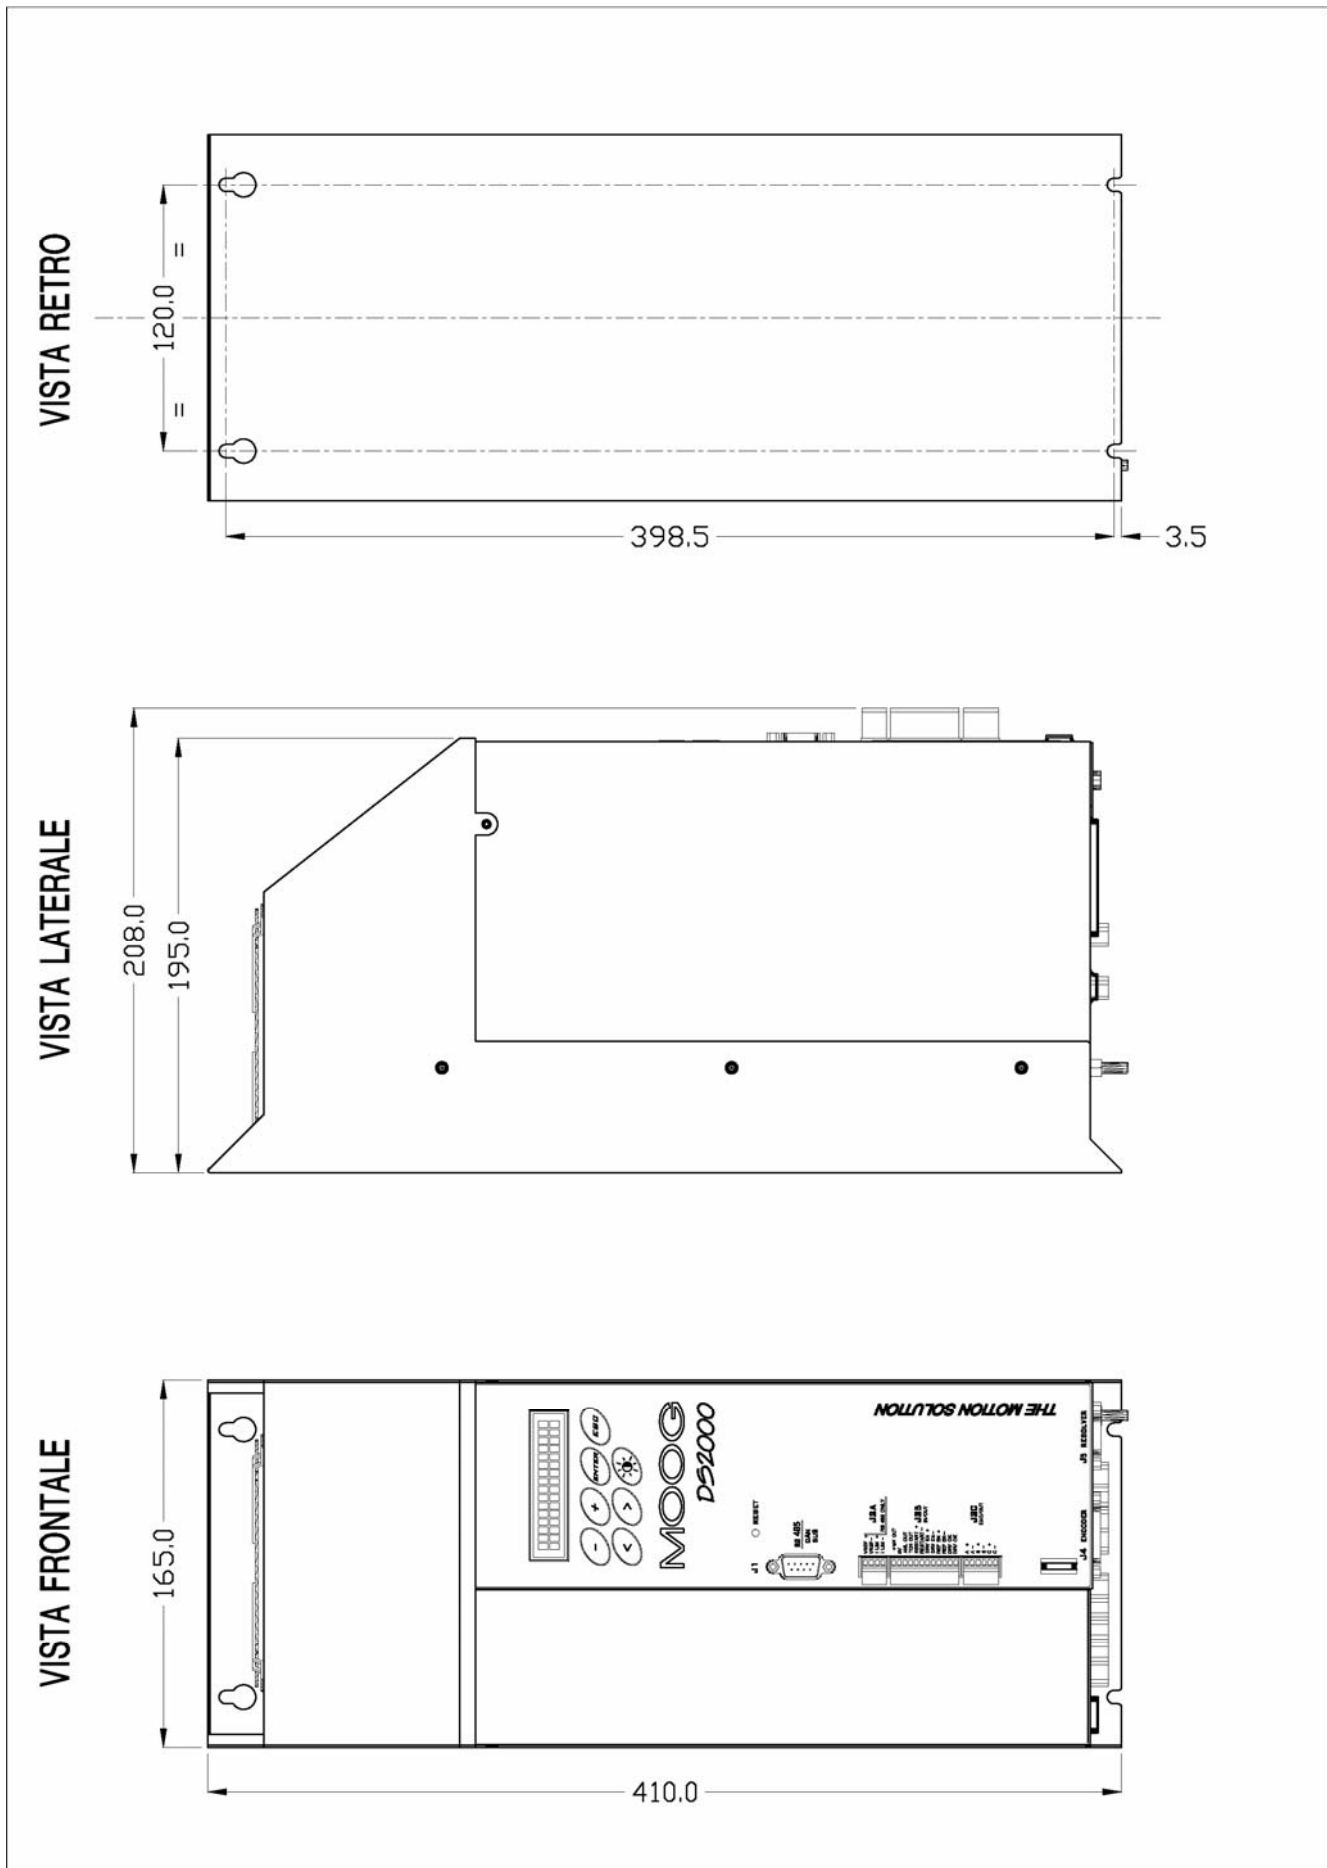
Dimensioni e fissaggi (mm) taglia C
